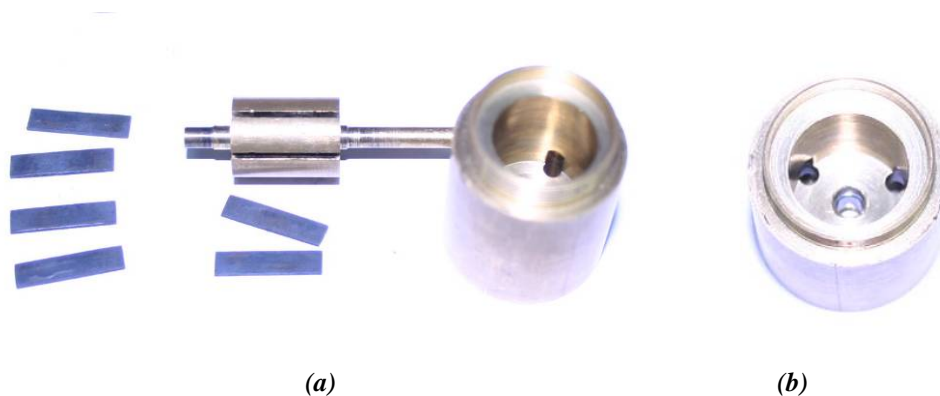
(a) Partes principales del segundo diseño del micromotor neumático de aspas sin resortes, (b) Carcasa y estator en una sola pieza.
